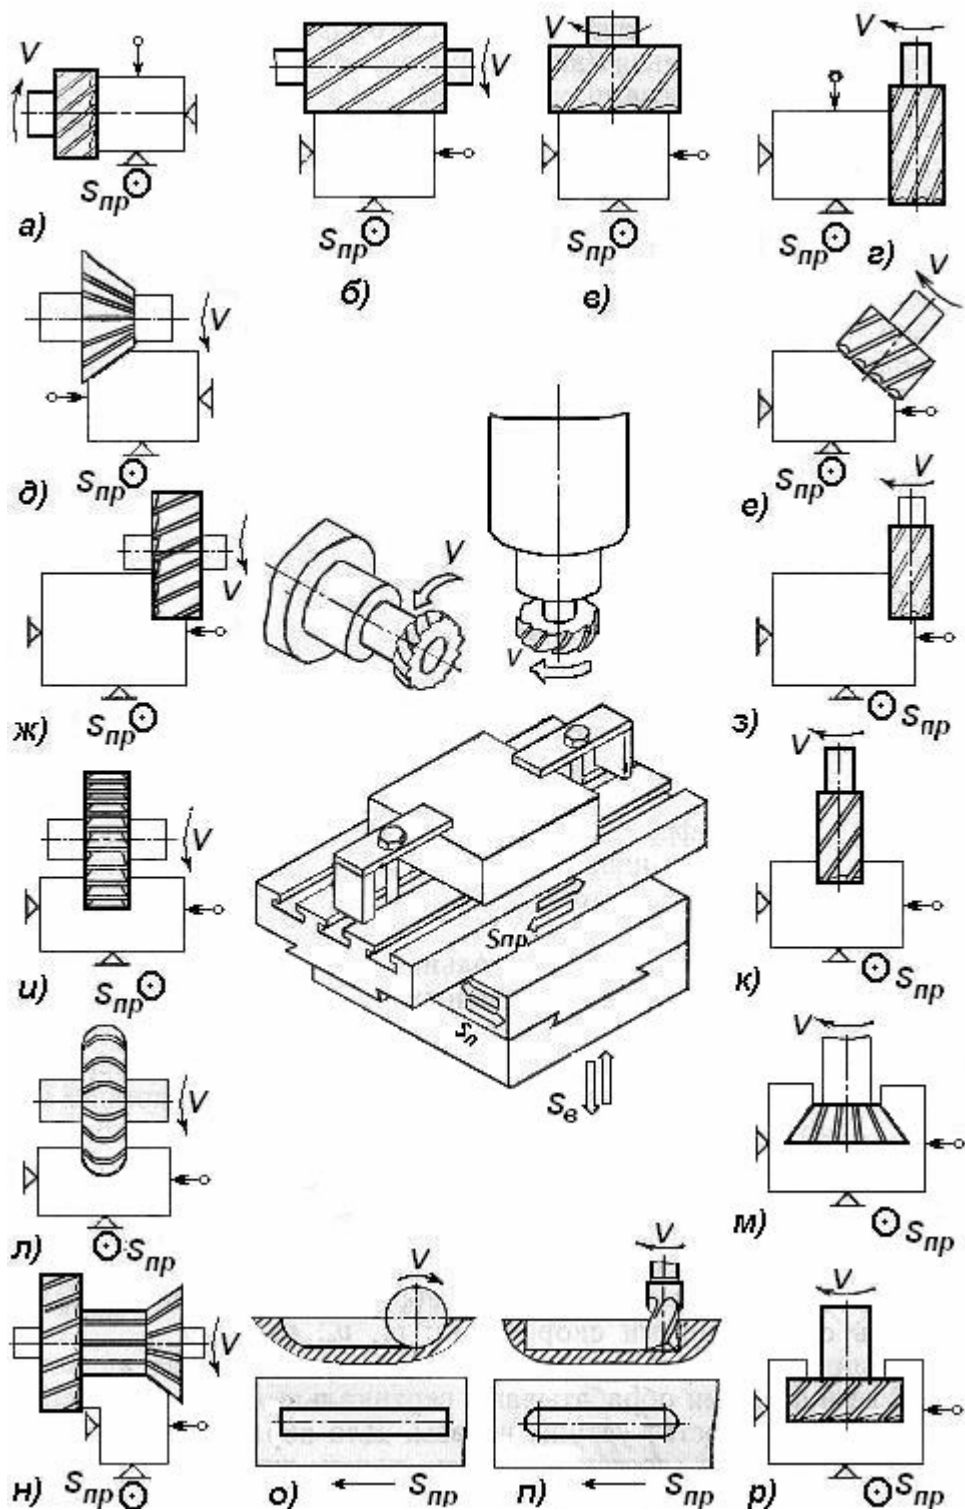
Типы фрез и схемы обработки поверхностей на фрезерных станках:
